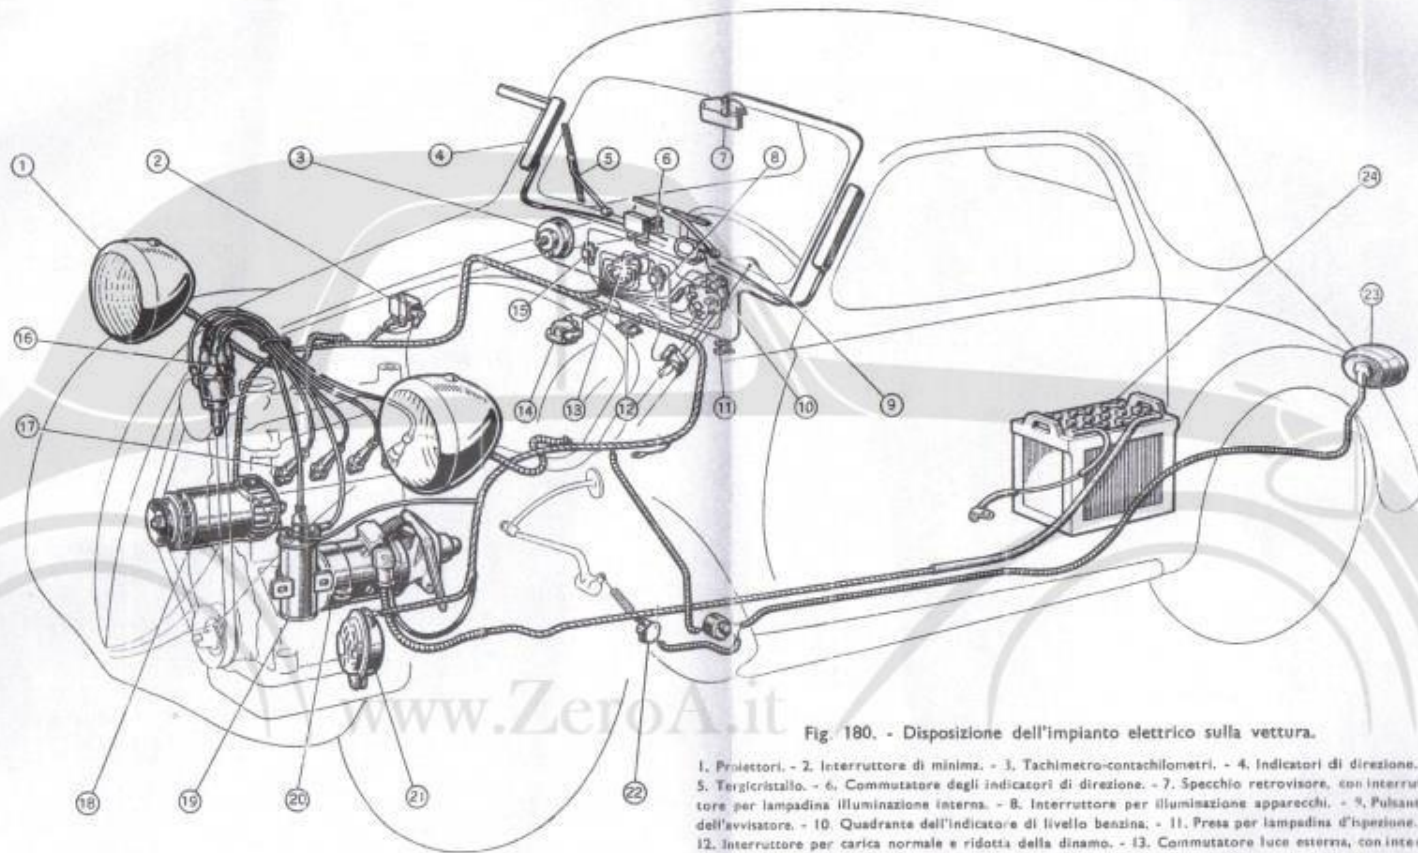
Disposizione dell'impianto elettrico sulla vettura.
